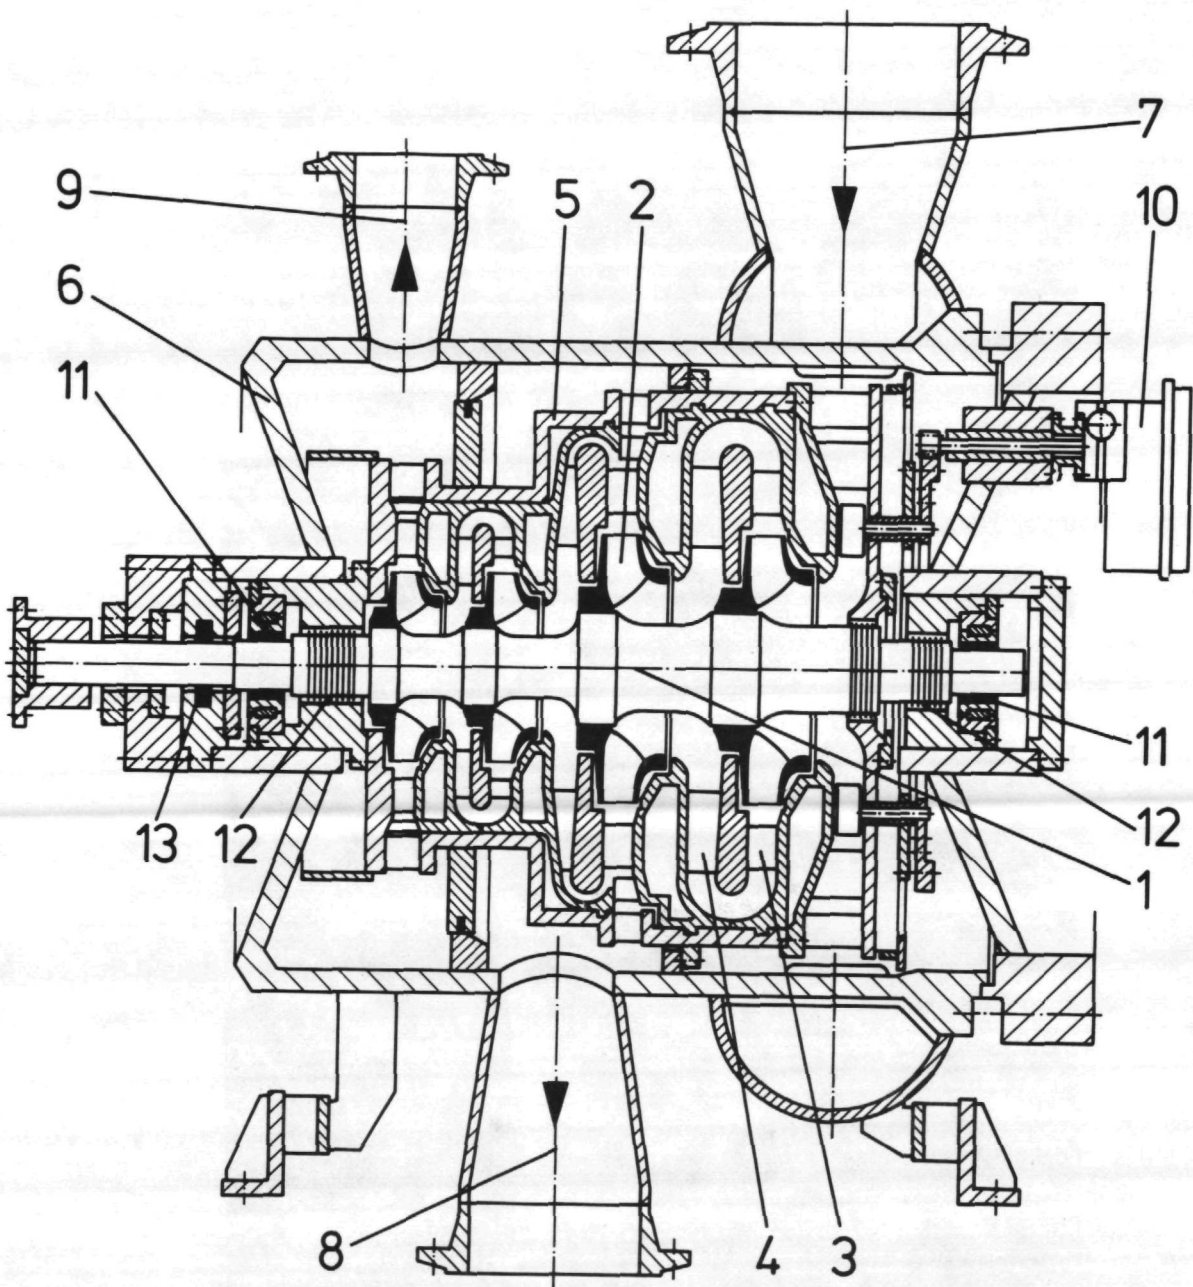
Prinzipschnittbild HHV-Kühlgasgebläse mit
